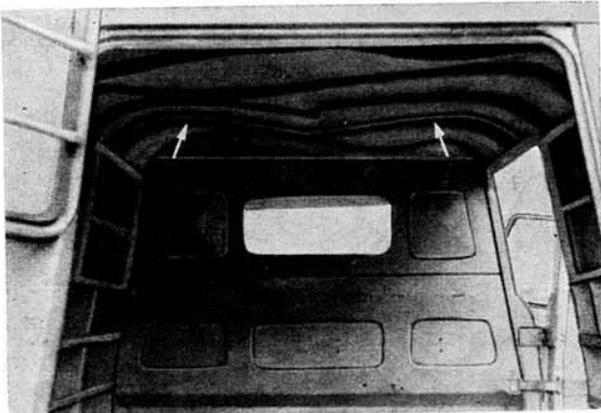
Das eingedrückte Dach muß durch ein neues ersetzt werden.
